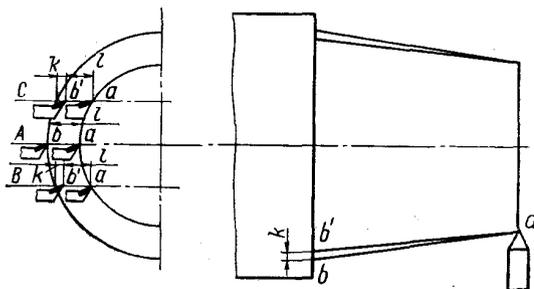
Схема искажения конусности детали при установке резца не по центру детали
